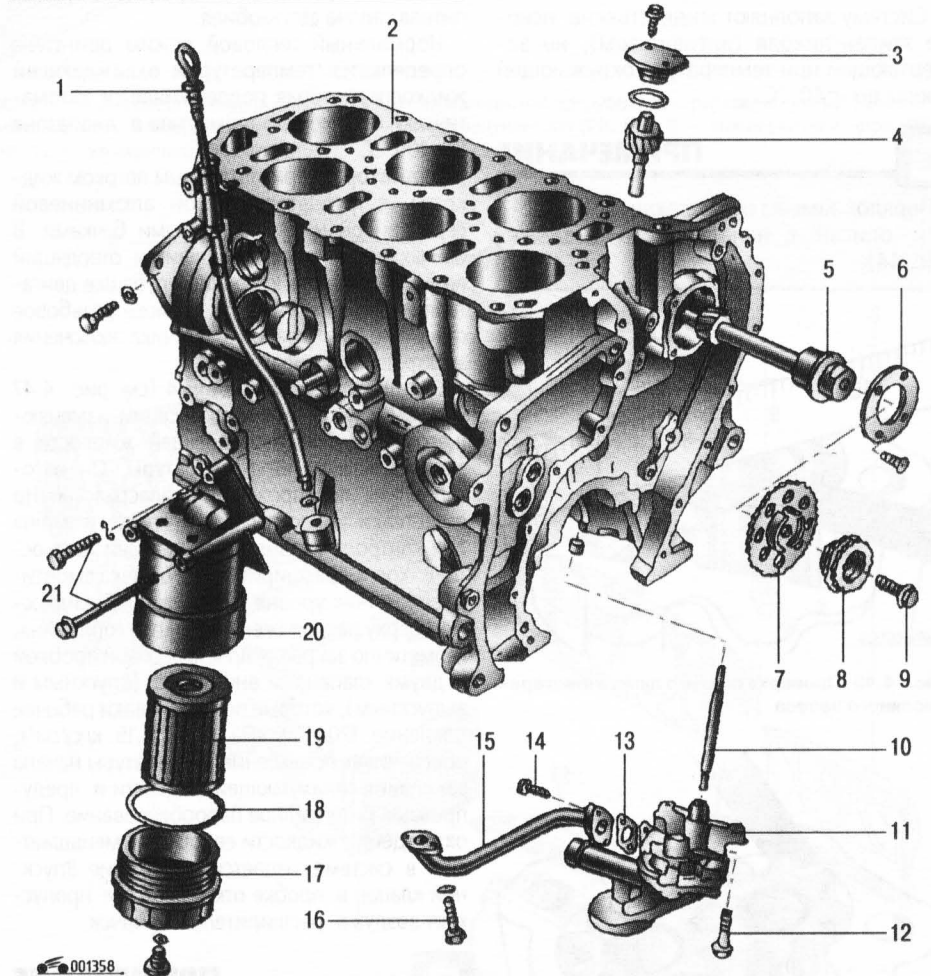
Масляный насос и масляный фильтр: 1 – масляный шуп; 2 – блок цилиндров; 3 – крышка вала привода масляного насоса; 4 – шестерня привода масляного насоса; 5 – промежуточный вал; 6 – крышка промежуточного вала; 7 – ведомая звездочка промежуточного вала; 8 – ведущая звездочка промежуточного вала; 9 – болт крепления звездочек промежуточного вала; 10 – вал привода масляного насоса; 11 – масляный насос; 12 – болт крепления масляного насоса; 13 – прокладка маслоприемной трубы; 14, 16 – болты крепления маслоприемной трубы; 15 – маслоприемная труба; 17 – крышка масляного фильтра; 18 – уплотнительное кольцо; 19 – масляный фильтр; 20 – корпус масляного фильтра; 21 – болты крепления корпуса масляного фильтра
